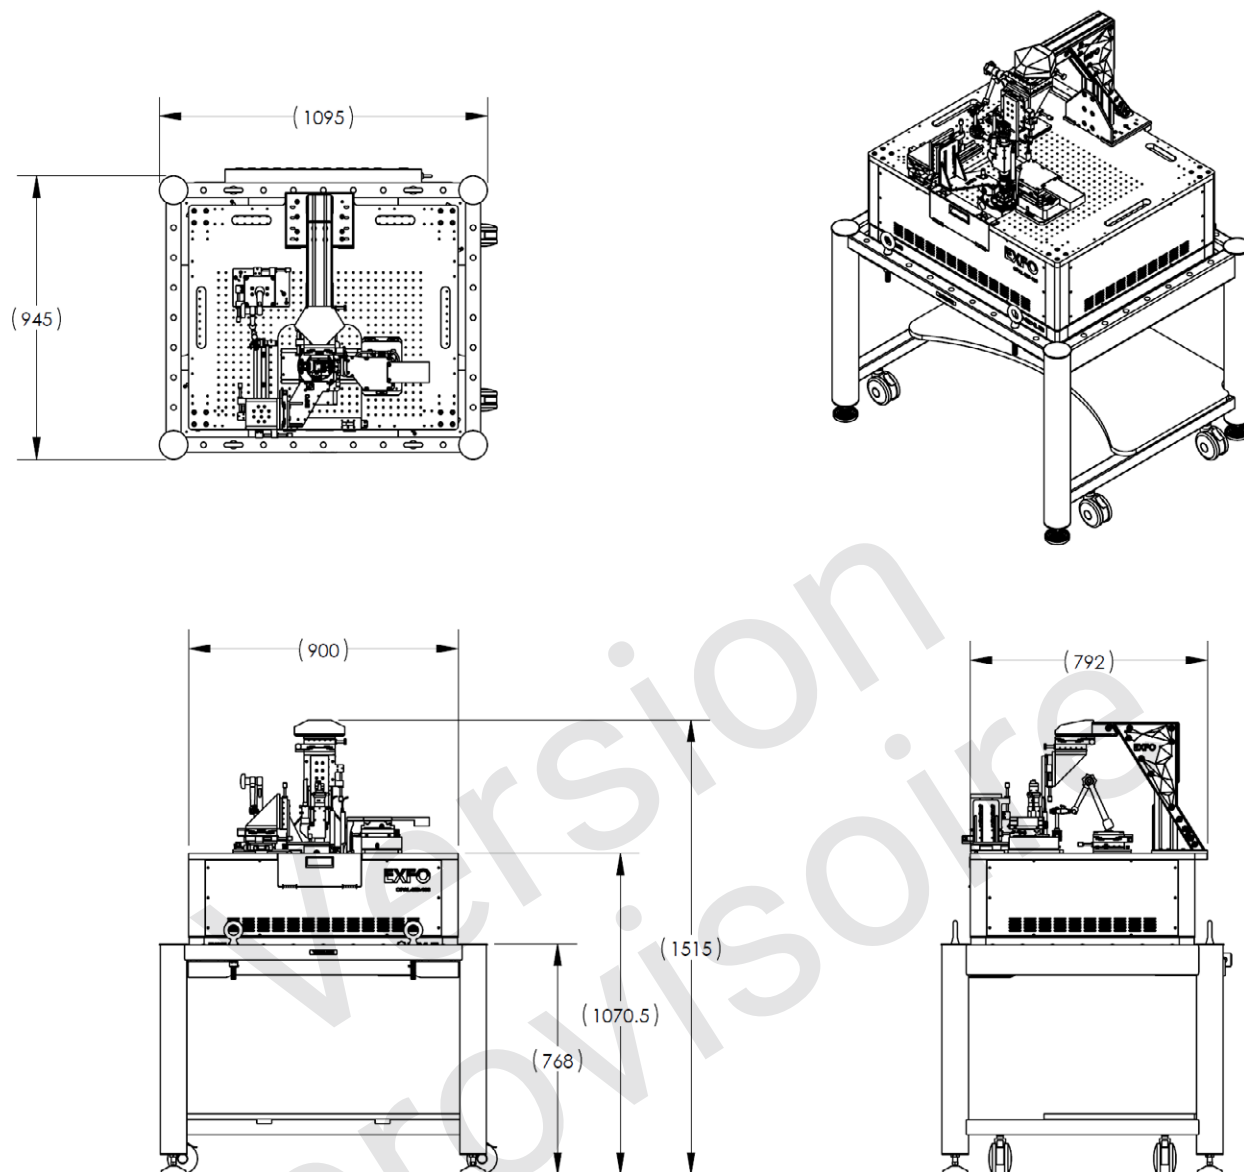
Dessin technique du système principal OPAL-MD-100 avec dimensions en millimètres.
